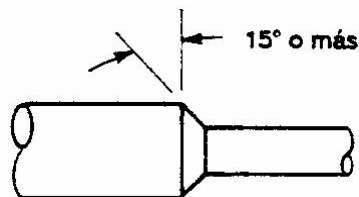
El máximo ángulo de los hombros en una máquina de matrices de cierre es de  $15^\circ$  sobre la perpendicular.
